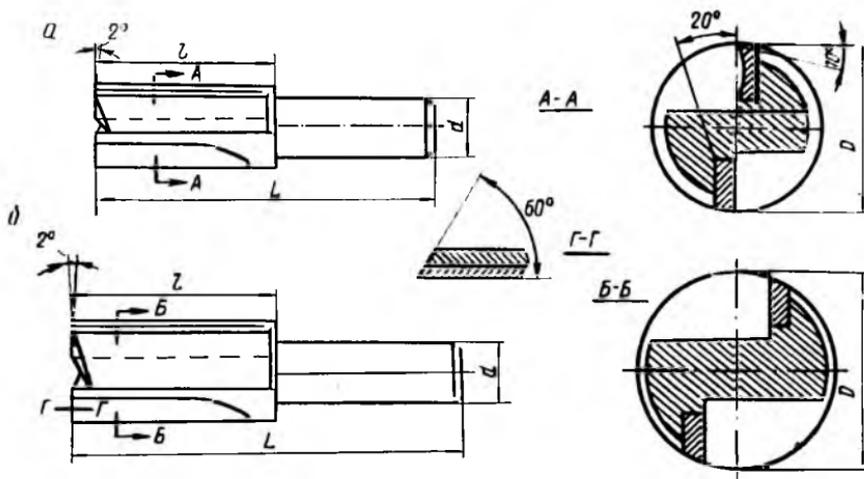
Концевые фрезы с пластинками из твердого сплава:
